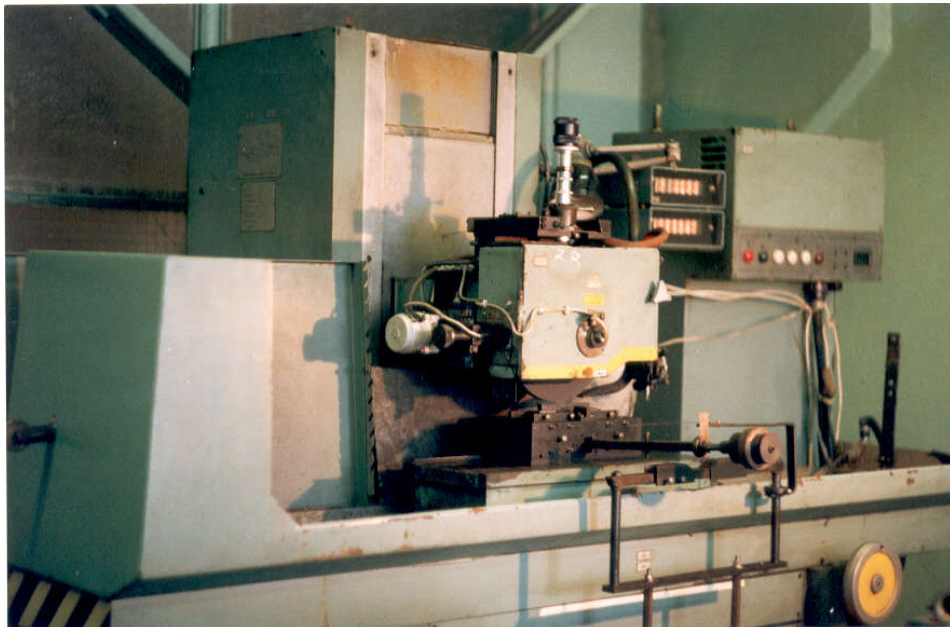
Общий вид модернизированного плоскошлифовального станка модели 3Д711АФ11
